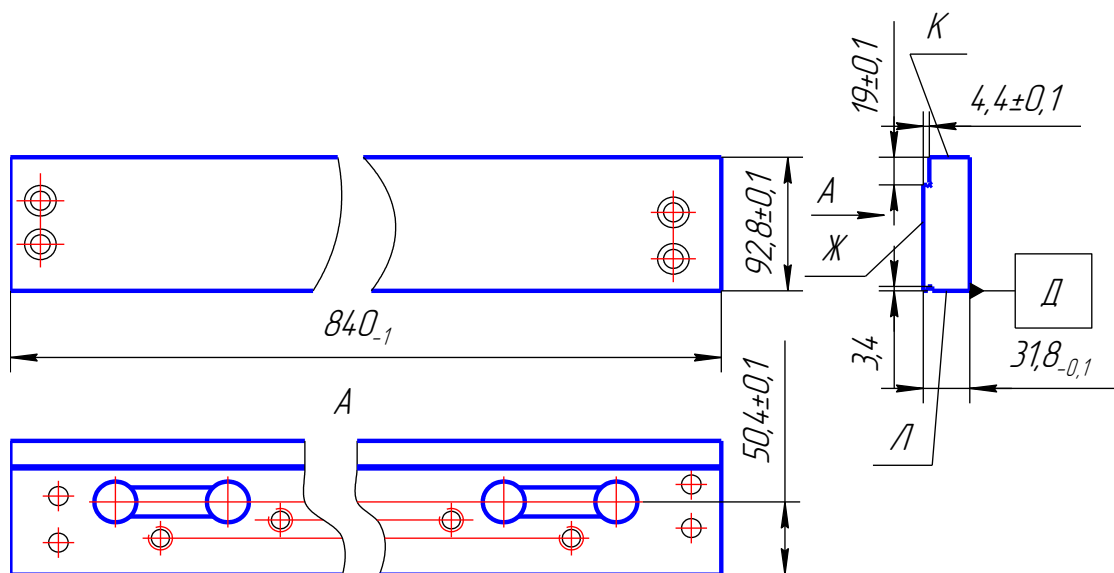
Заготовка планки ОММ64.70.00.00.011/23.101 для комбінованої обробки
